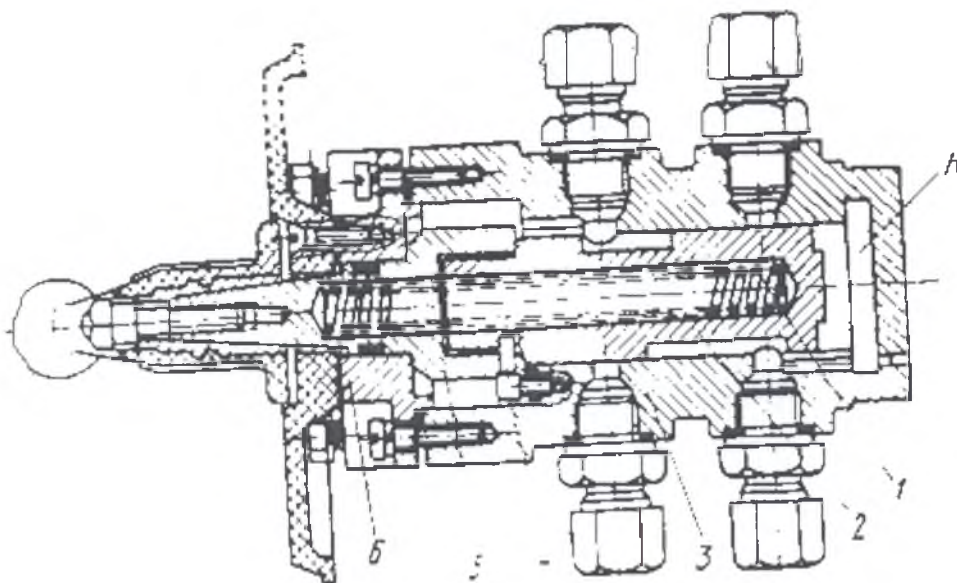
Блокирующий клапан: 1-пружина, 2- пробка, 3- корпус, 4-штифт, 5-поводок, 6-крышка
